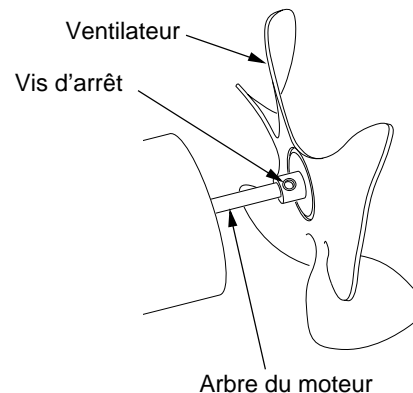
Emplacement du ventilateur, de l'arbre du moteur et de la vis d'arrêt
